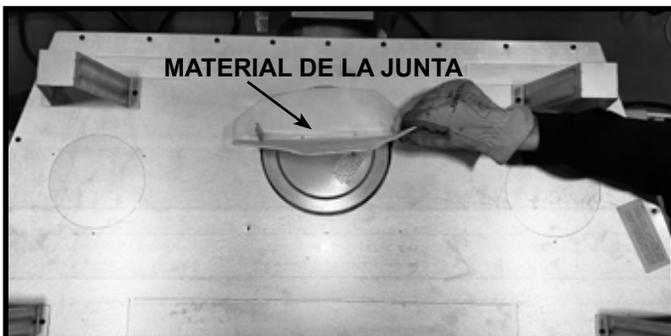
Retiro del material blanco de la junta que cubre la tapa de sellado
